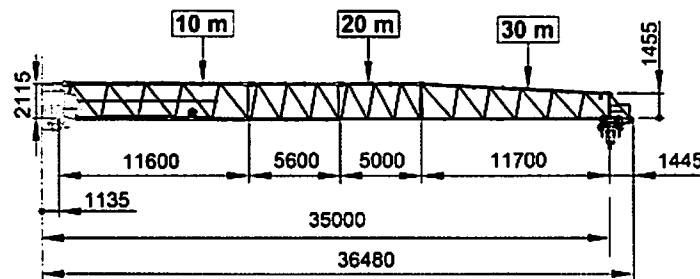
Position der Ausladungsschilder für Ausleger 35 m
